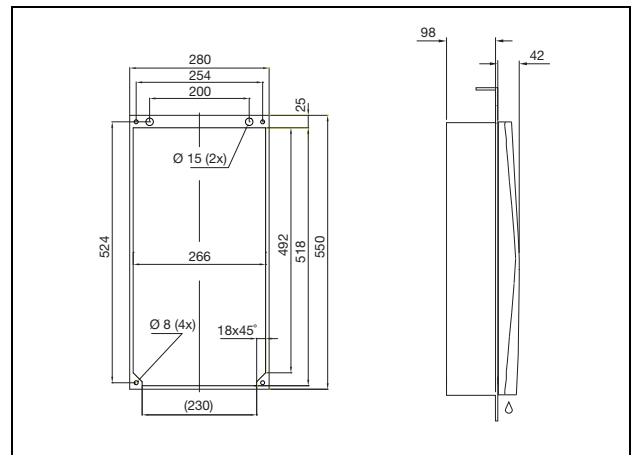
3304.xxx, 3305.xxx částečně zapuštěná montáž
